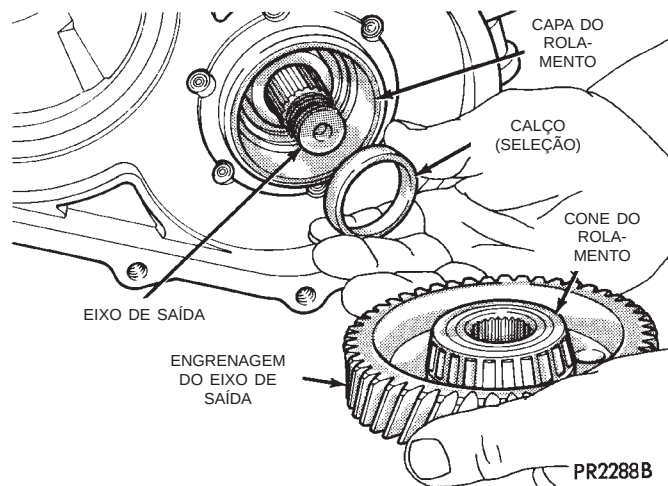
Engrenagem do Eixo de Saída e Calço (Seleção)
